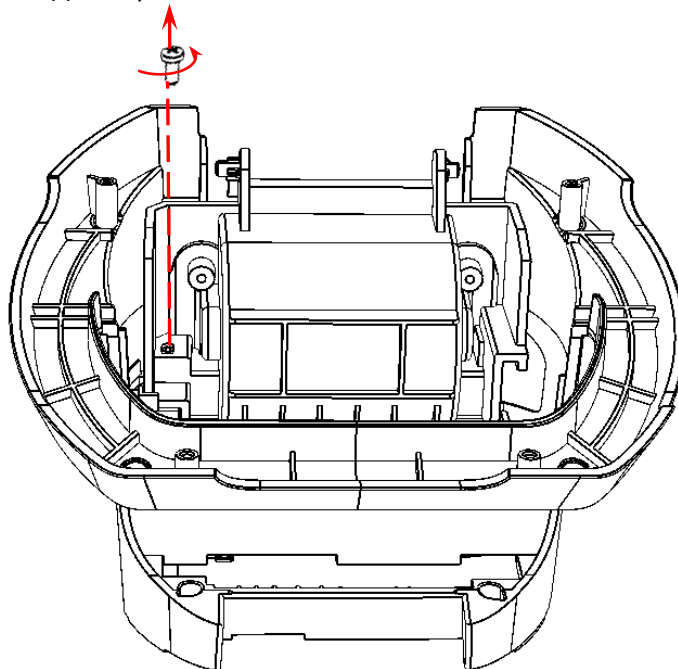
Винт крепления лотка для ЧЛ к стойке корпуса (расположенный во внутренней стороны)
